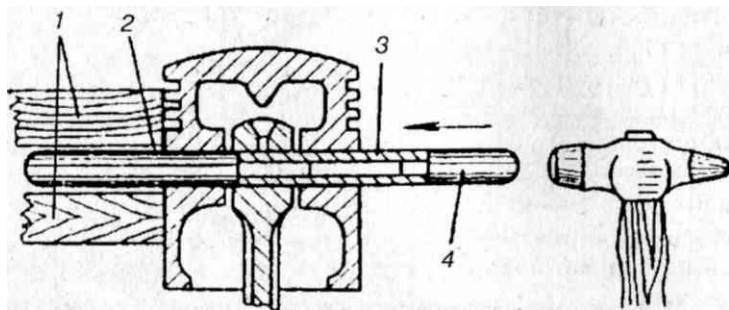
Выпрессовка и запрессовка поршневого пальца при помощи молотка: 1 - деревянный брус; 2 - оправка; 3 - поршневой палец; 4 - выколотка
